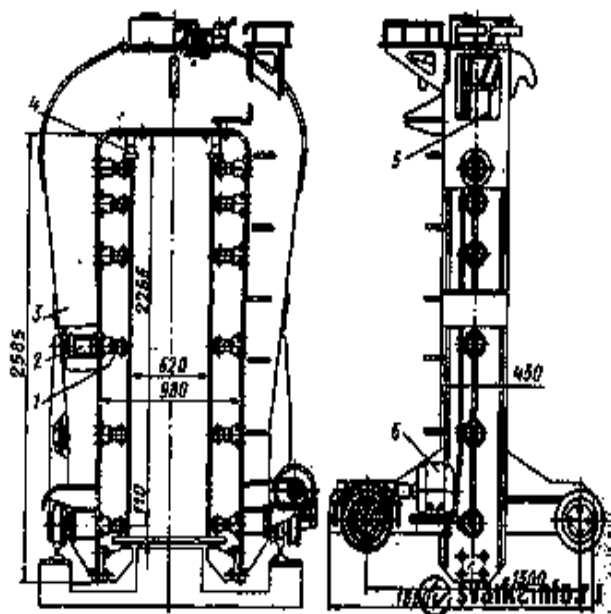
Портальна установка для збирання великогабаритних коробчастих балок:
